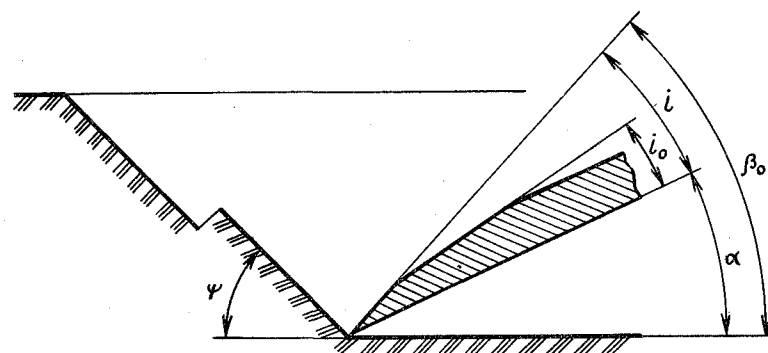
Заточка режущей кромки рыхлительной лапы чизельного плуга-глубокорыхлителя
